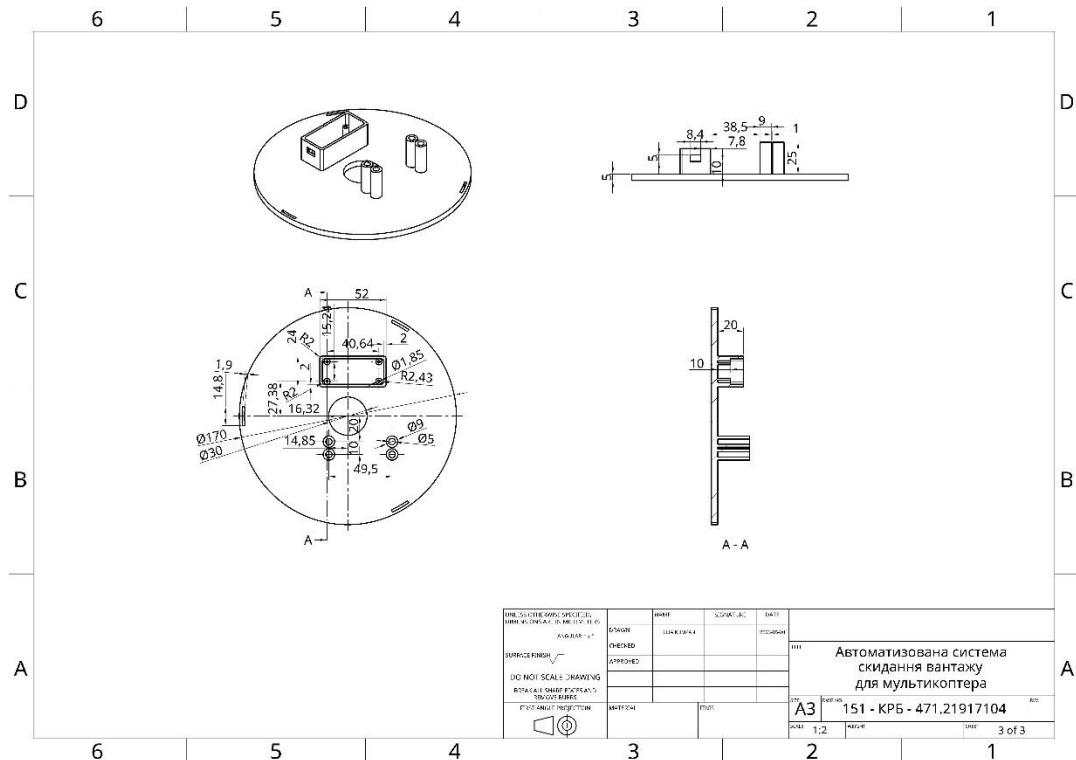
Креслення кришки конструкції автоматизованої системи скидання вантажу
